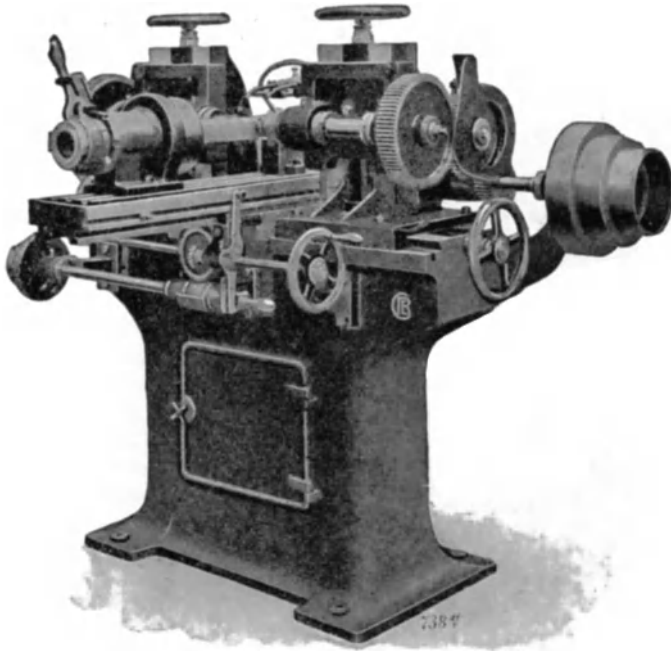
Die Doppelfräsmaschine von J. E. Reinecker.
